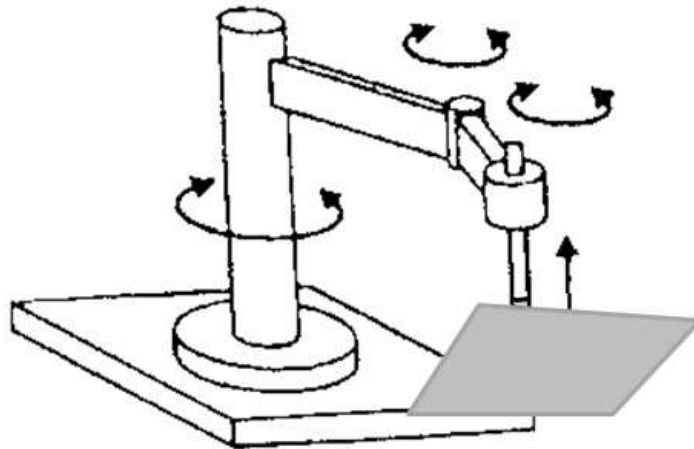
Caso de soldadora sobre placa cuadrada con robot SCARA.
